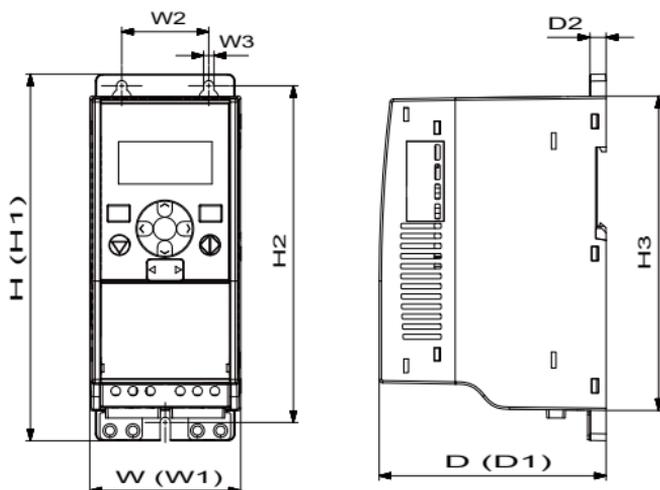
Dimensões do VACON® 20, MI1 - MI3
